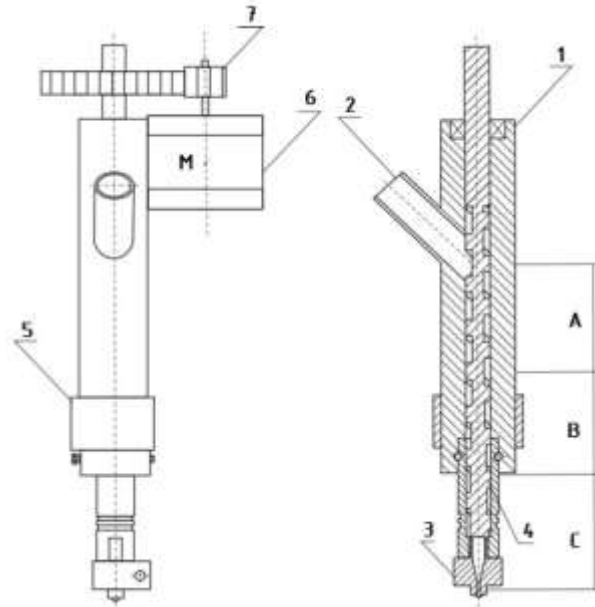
Загальний вигляд шнекового екструдера з приводом: 1 – корпус; 2 – завантажувальний отвір; 3 – сопло; 4 – шнек; 5 – нагрівальний елемент; 6 – кроковий двигун; 7 – зубчаста передача; А – зона живлення; В – зона стиснення, С – зона дозування
